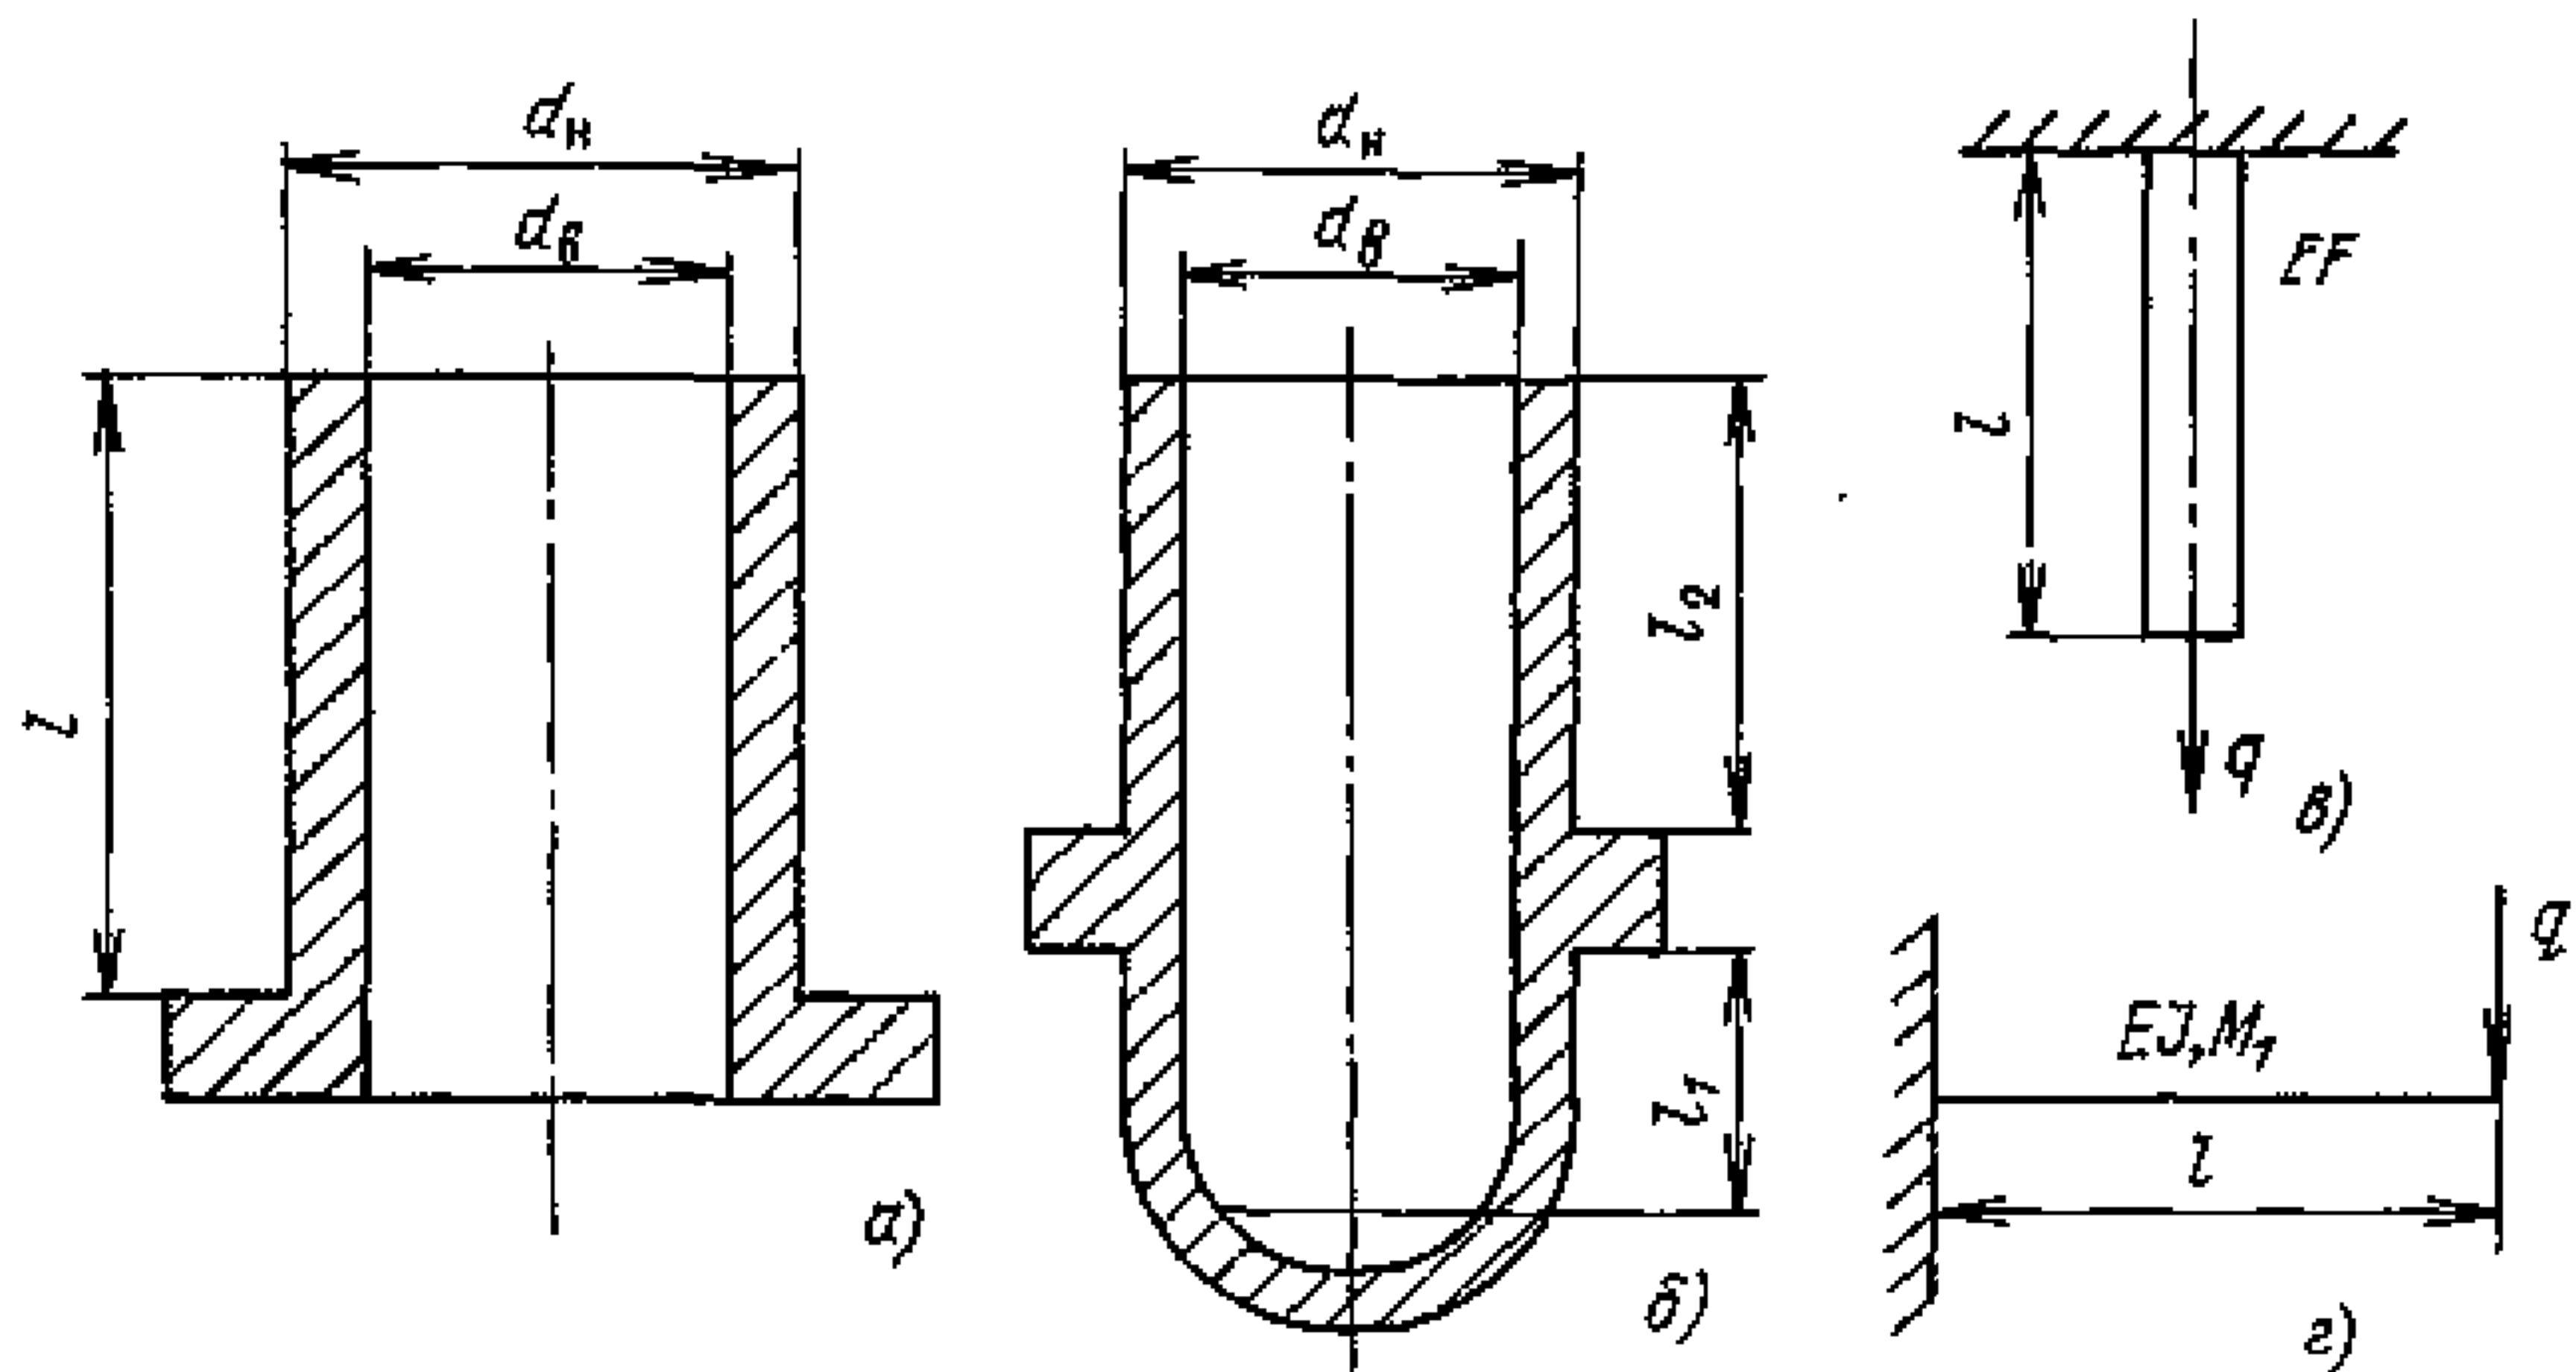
Схема крепления корпуса к фундаменту в нижней (а) и средней (б) частях и расчетная схема для продольных (в) и поперечных (г) колебаний
